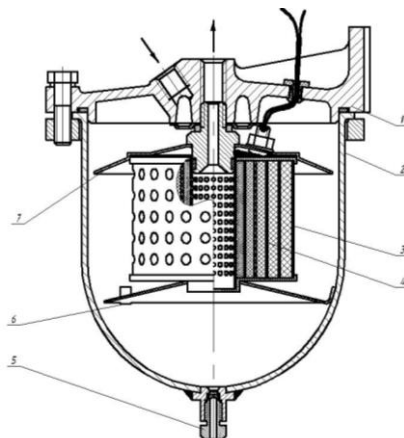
Фильтр-нагреватель: 1 – крышка корпуса фильтра; 2 – корпус фильтра; 3 – фильтроэлемент (патент RU 2112582 C1 В 01 D29/48); 4 – нагревательный элемент; 5 – сливная пробка; 6 – успокоитель; 7 – отражатель
